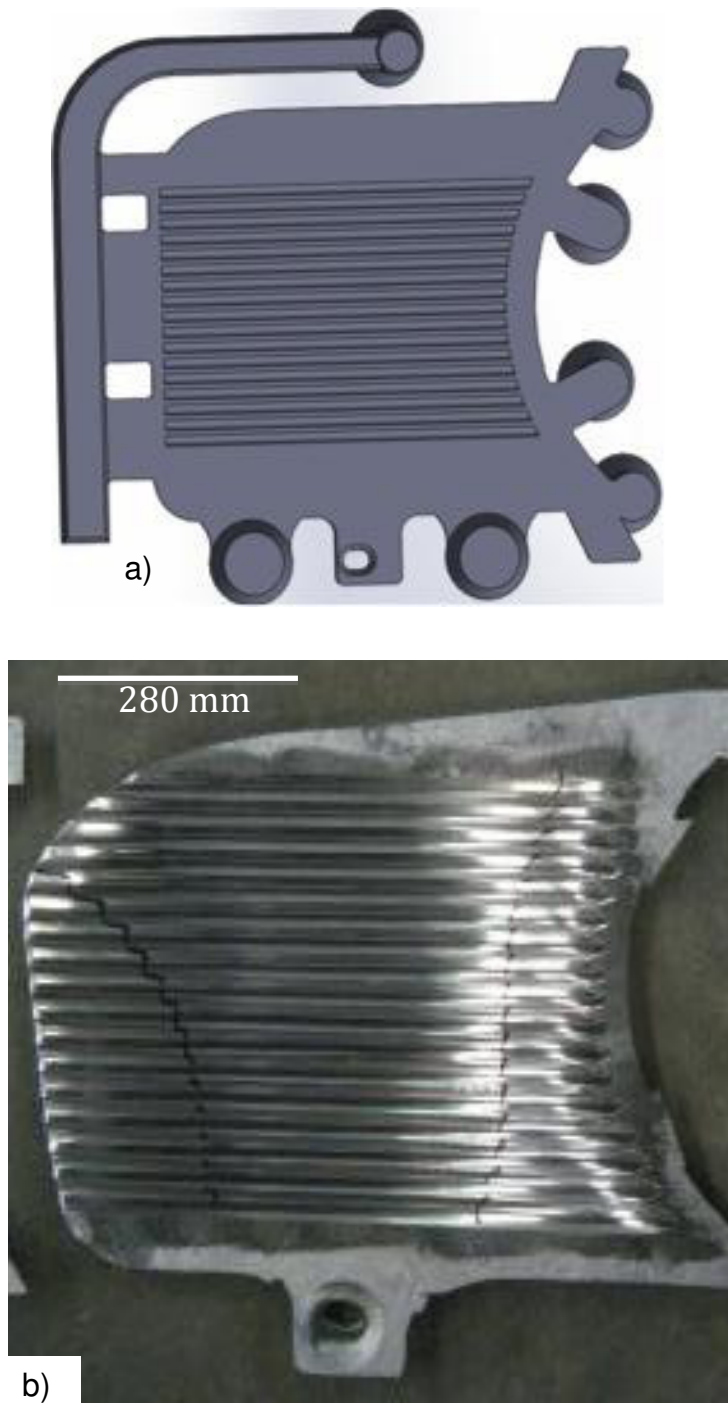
a) Diseño original de la plancha, b) plancha vaciada.
